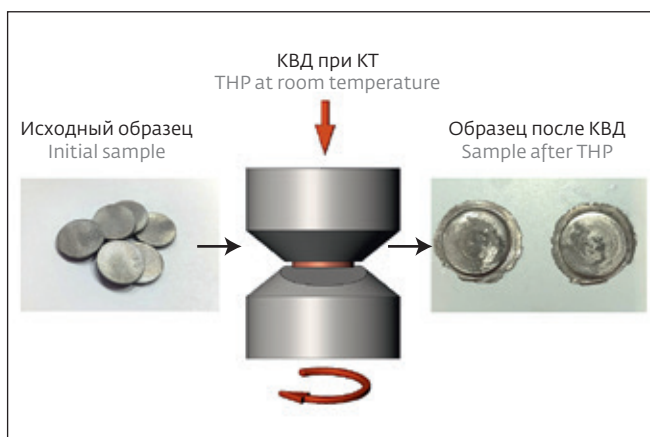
Схема КВД, внешний вид образцов до и после КВД
